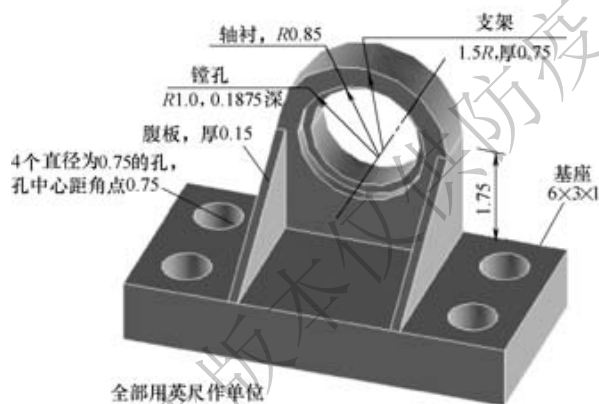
轴承座结构示意图 (图中尺寸单位为 ft)
